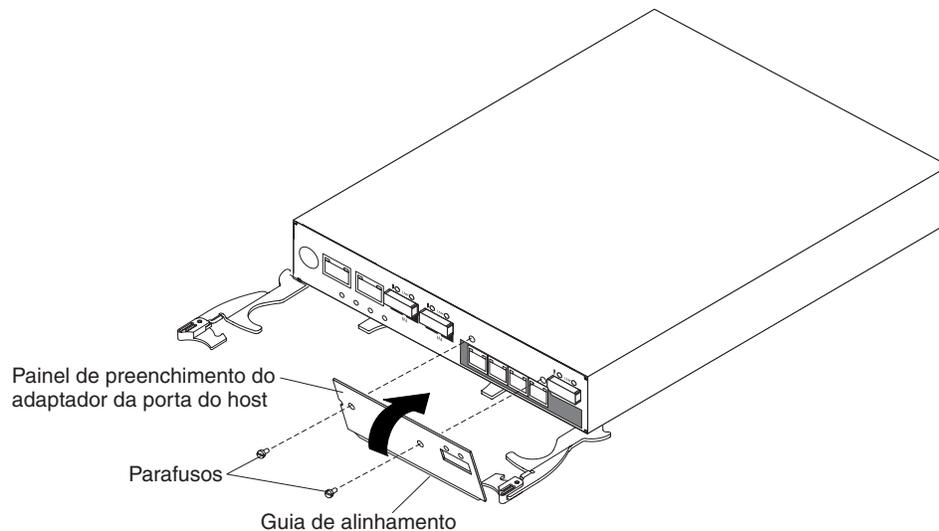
Removendo o Painel de Preenchimento do Adaptador de Porta do Host
